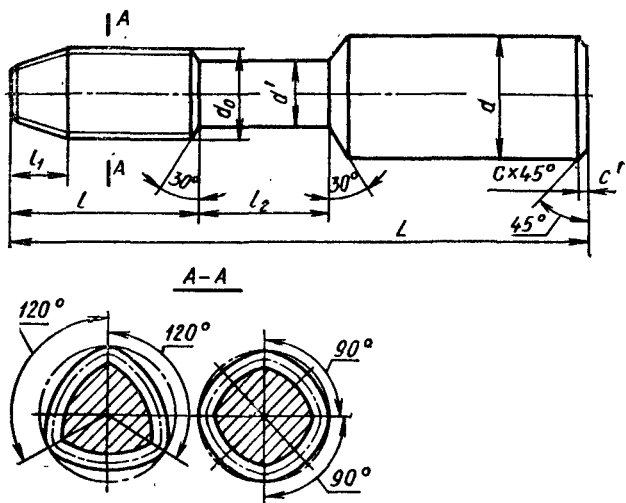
Метчик для холодного выдавливания внутренней резьбы
